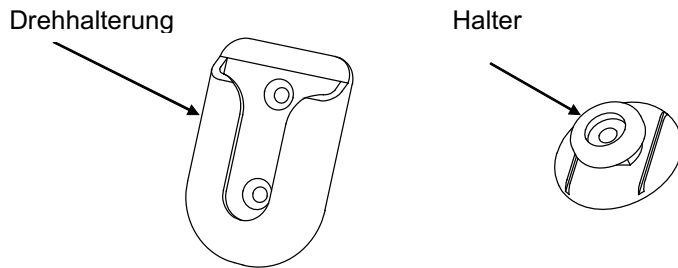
SmartTouch2™ Befestigungs Teile G10311
